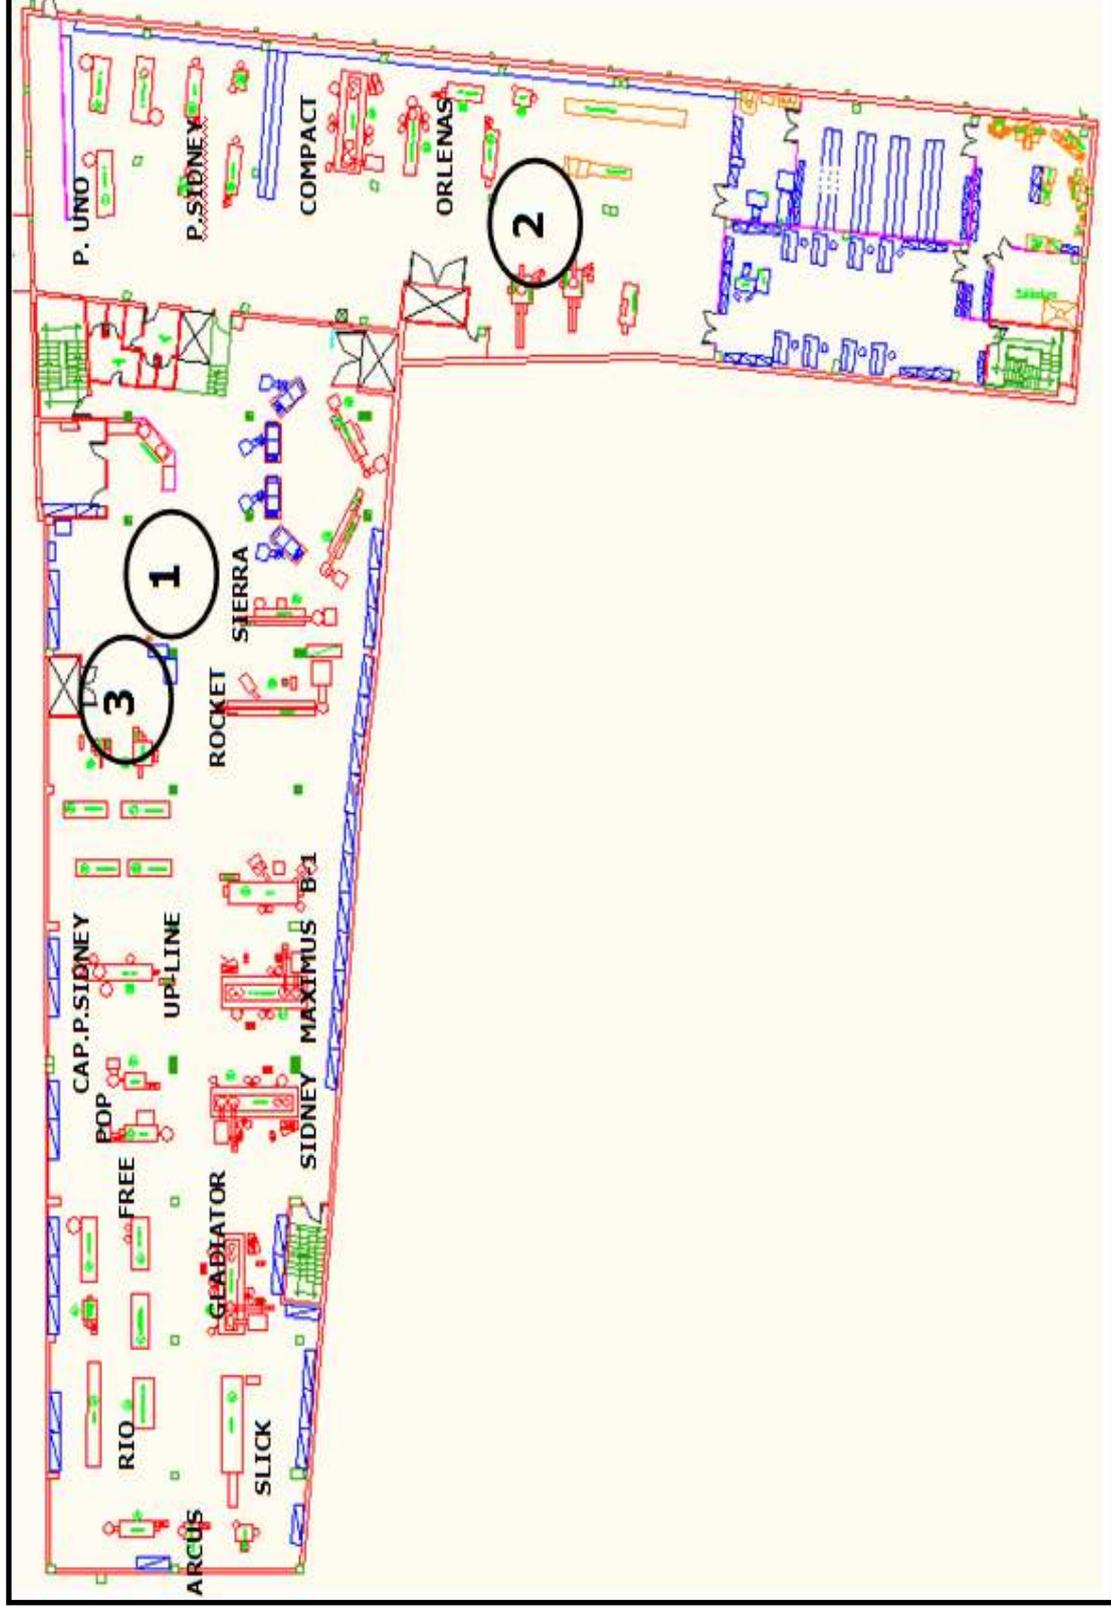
Distribución en planta de las máquinas de ensamblar automáticamente por modelos.
